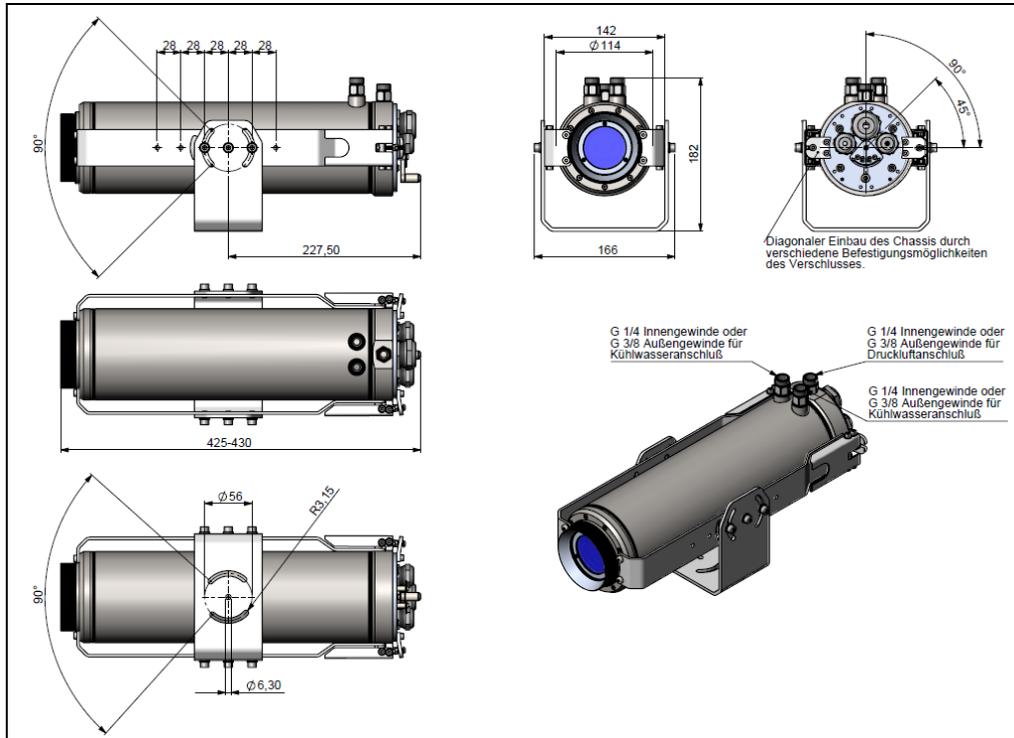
CoolingJacket Advanced, Extended-Version –Komplettansicht
